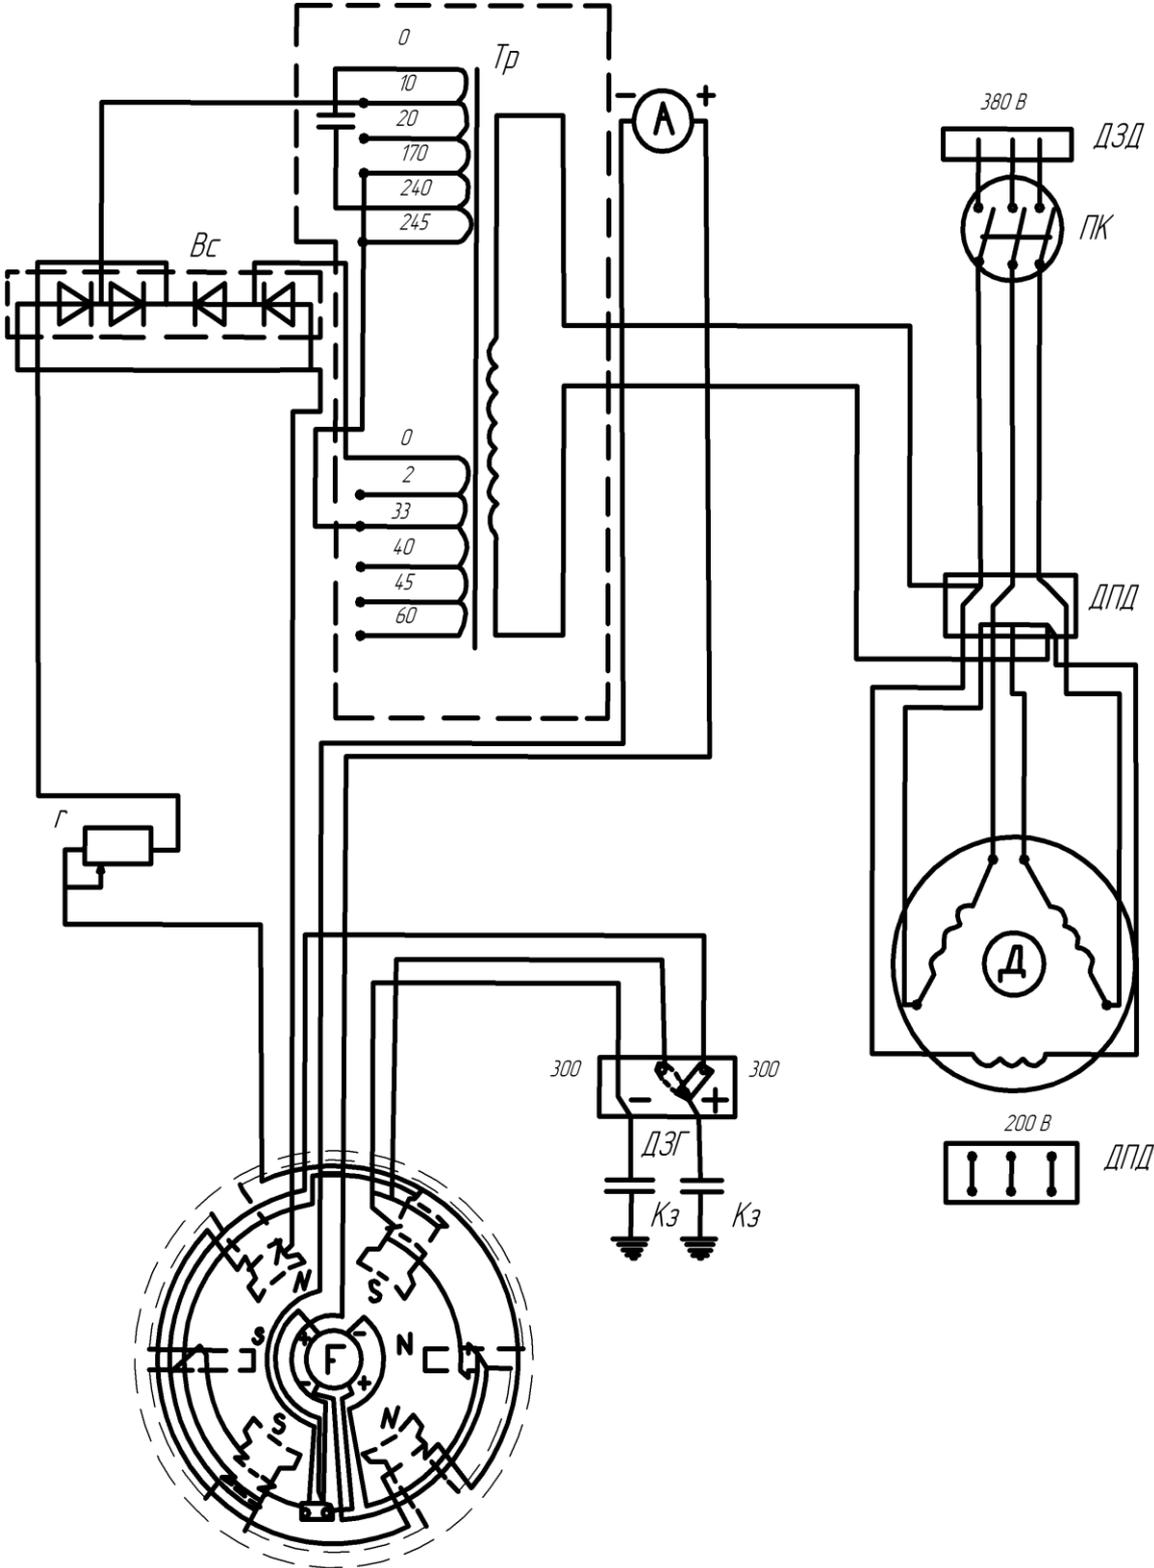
Электрическая схема сварочного преобразователя ПСО-500
